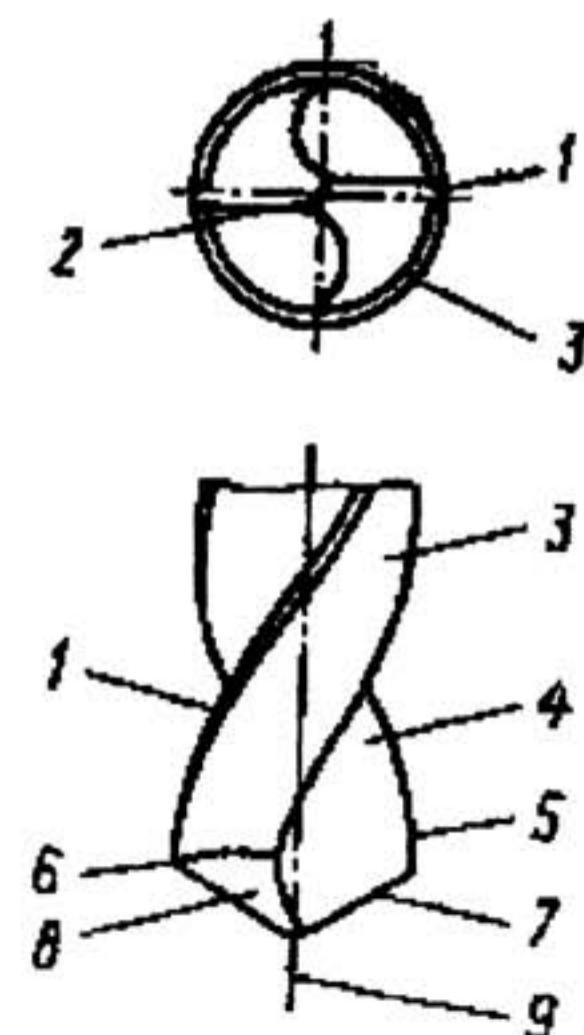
Поверхности, режущие кромки и вершины режущих кромок спирального сверла:
